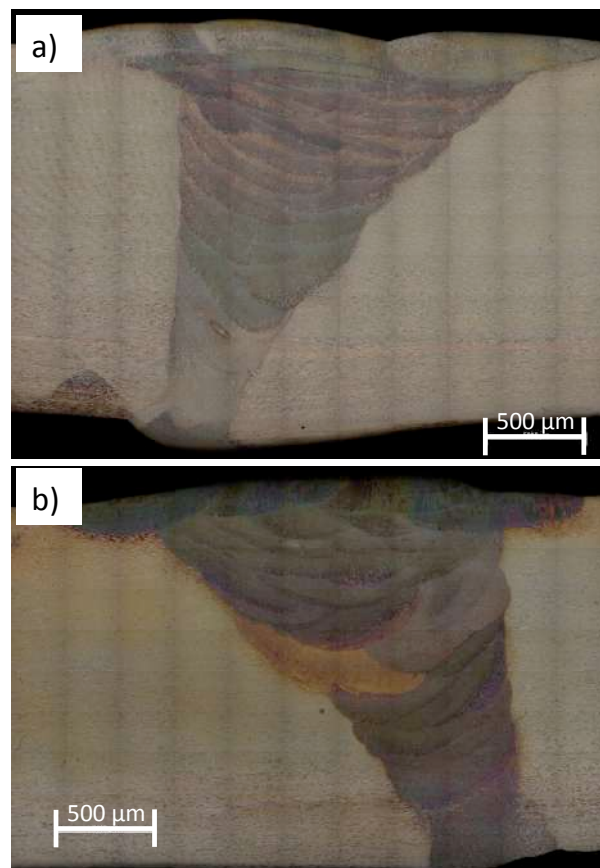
Mosaico da junta soldada a) com aporte térmico de 1,1 kJ/mm e b) com aporte de 2,0 kJ/mm.
